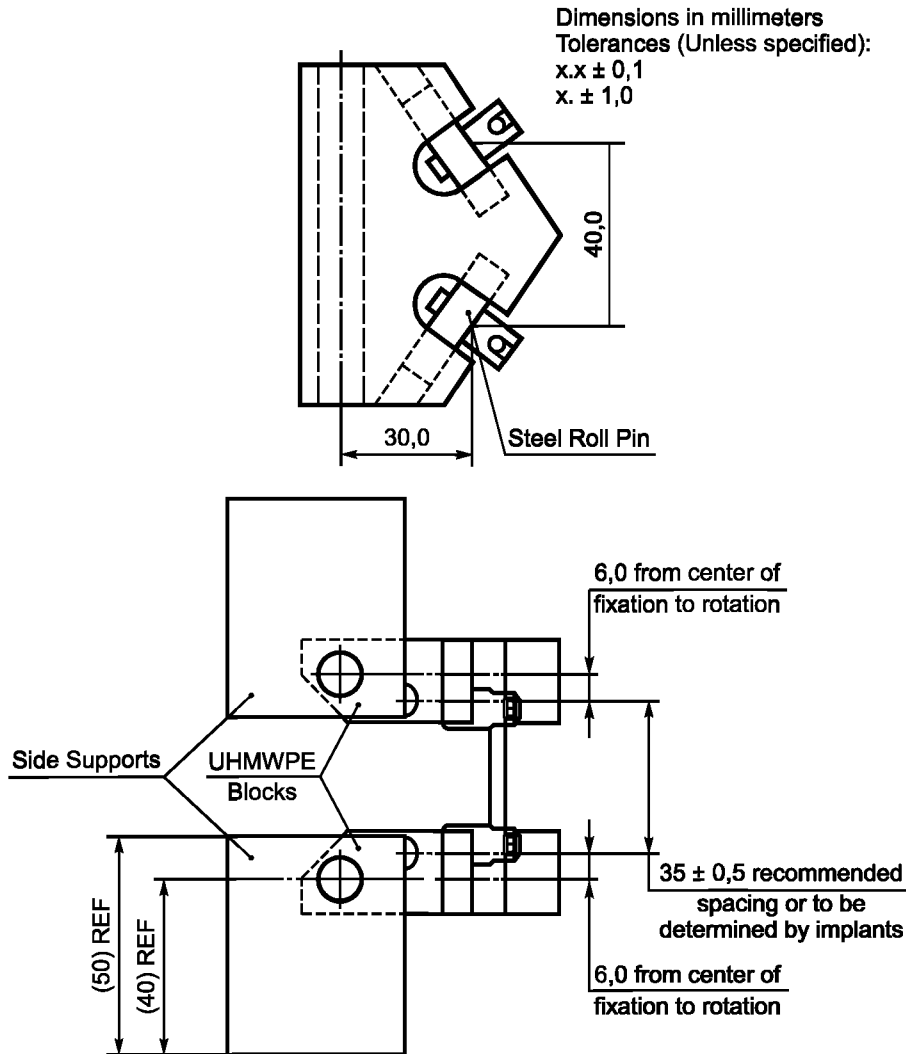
Схема испытания шейной двусторонней конструкции для винтов или болтов
